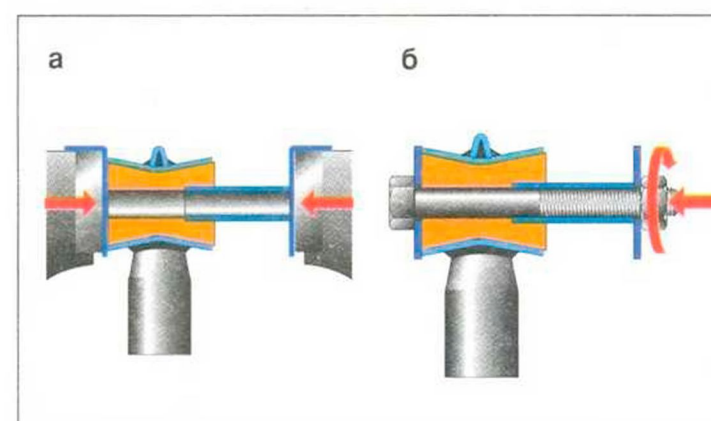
Запрессовка стальной втулки: а – в тисках; б – с помощью болта
